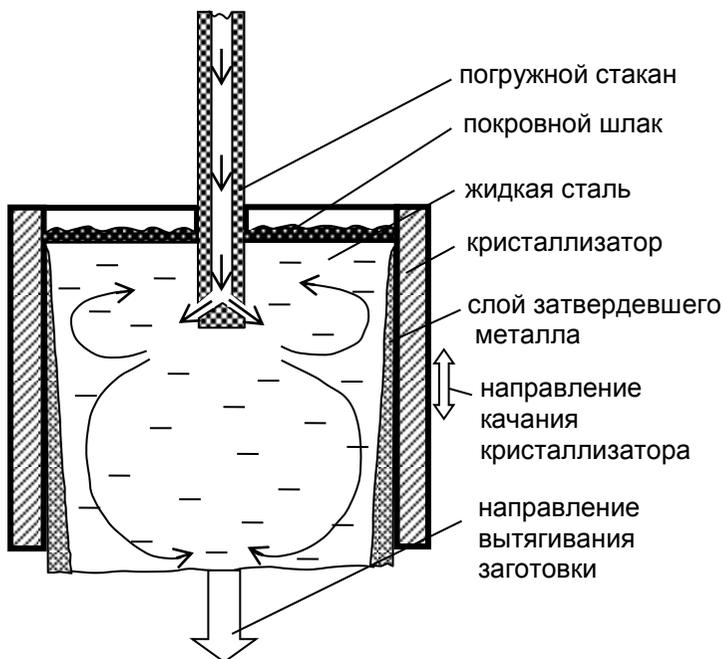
Эскиз слябовой непрерывнолитой заготовки
